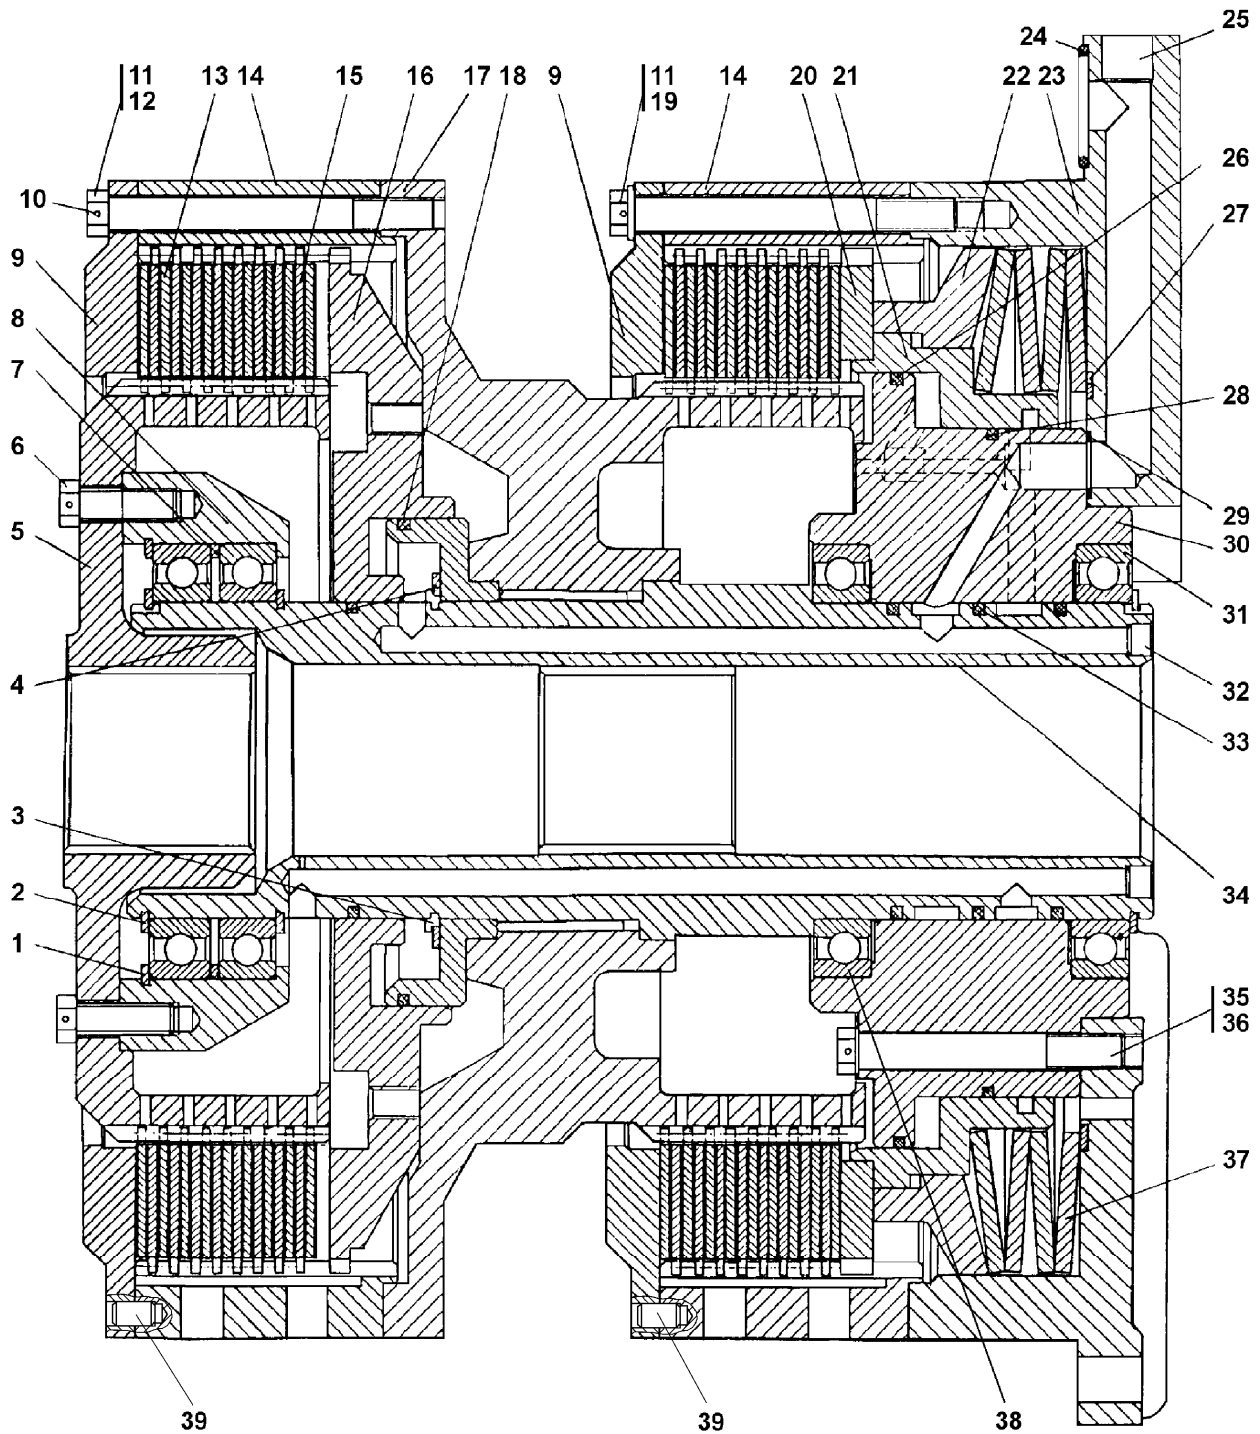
Фрикцион бортовой и тормоз остановочный
